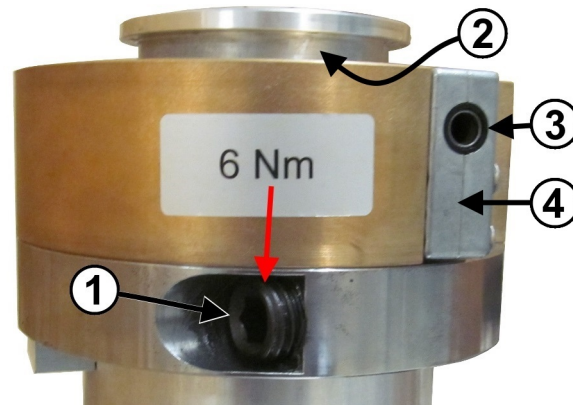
Drehtisch mit Klemmschraube und Kurbelantrieb
